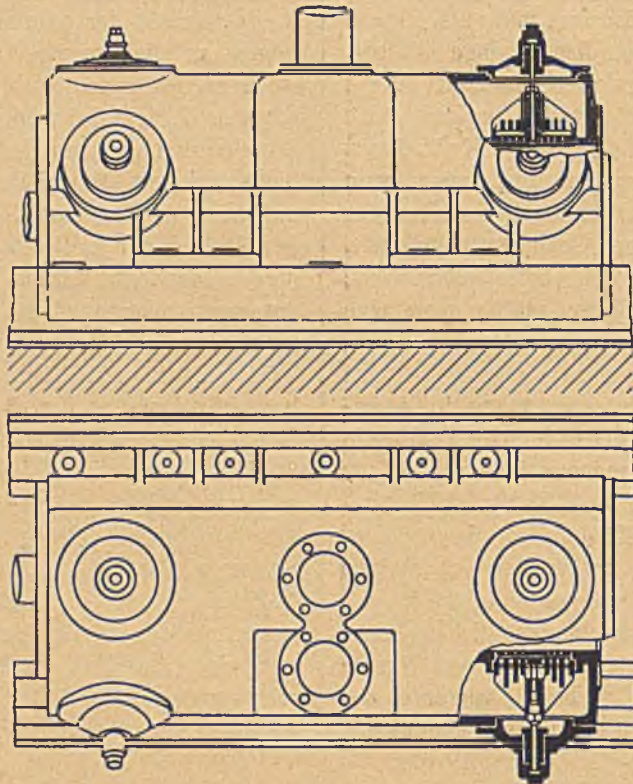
Luftzylinder eines Einzel-Kompressors.
